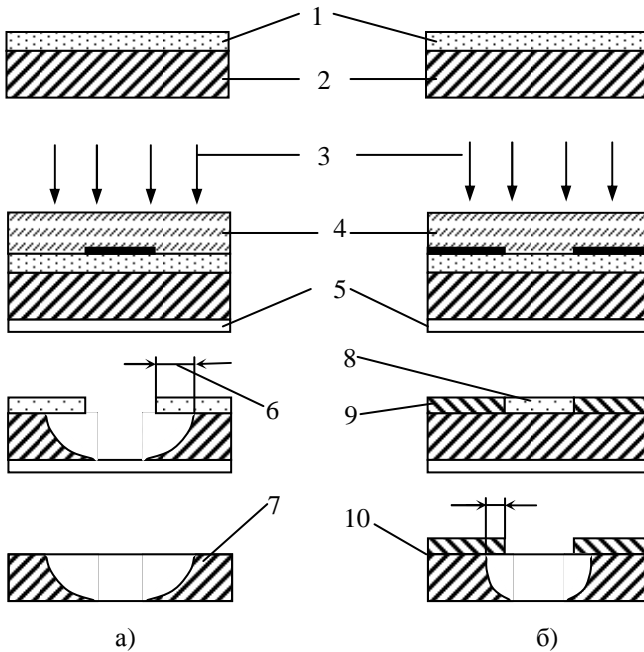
Схема изготовления монометаллического (а) и биметаллического (б) трафаретов: 1 – фоторезист; 2 – фольга; 3 – излучение; 4 – фотошаблон; 5 – лак; 6 – подтрав; 7 – монометаллический трафарет; 8 – ФР-маска; 9 – слой никеля; 10 – биметаллический трафарет
